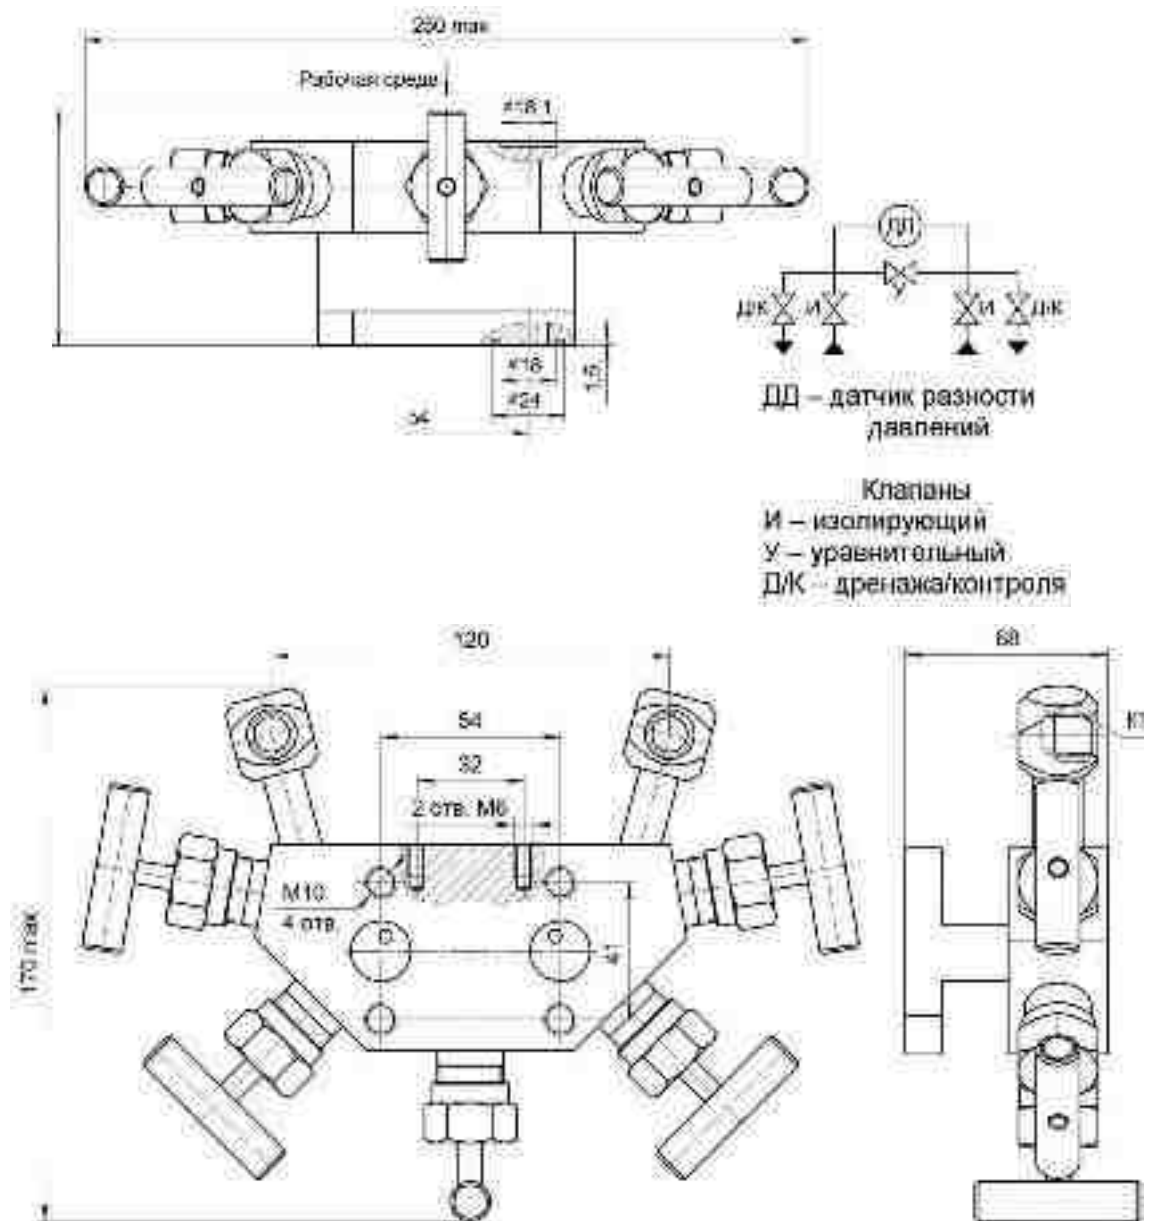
Гидравлическая схема, габаритные и присоединительные размеры БКН5-7-00
